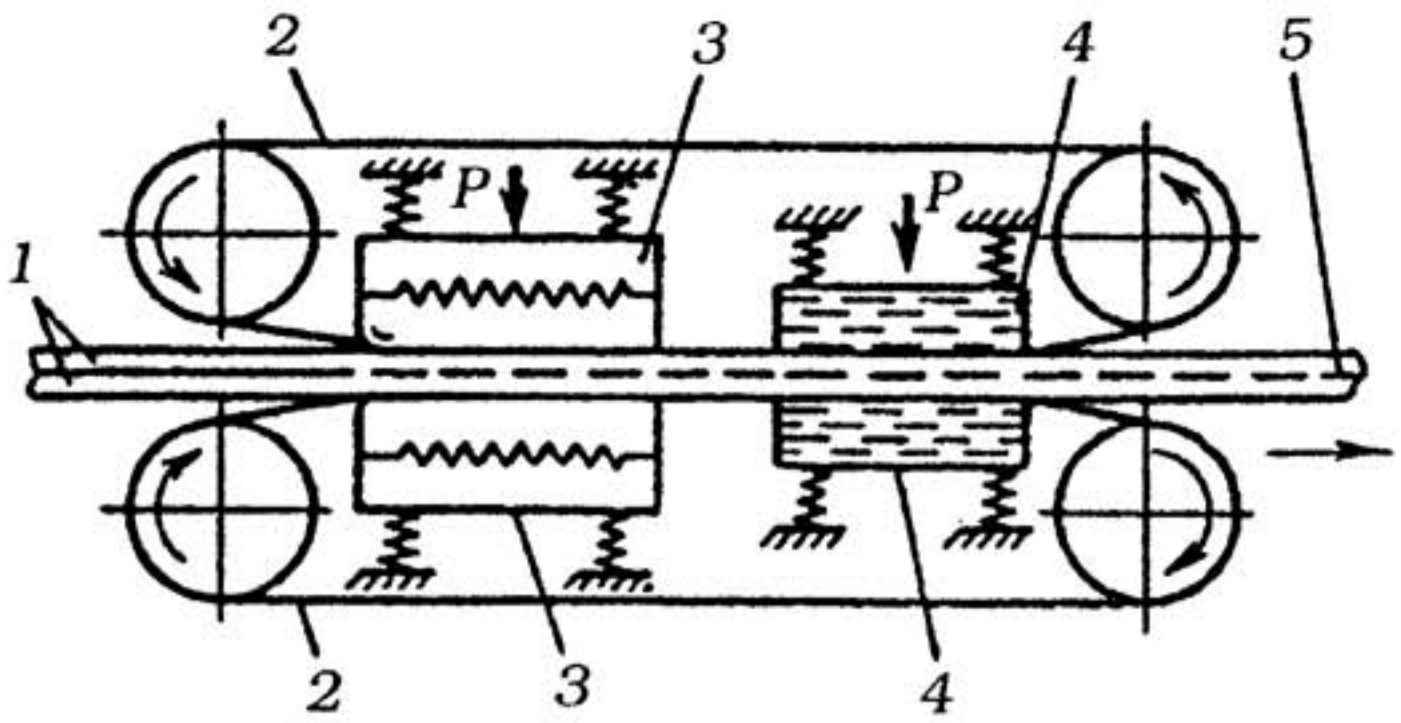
Схема ленточной двусторонней контактно-тепловой сварки: 1 — свариваемый материал; 2 — стальная лента; 3 — нагревательные губки; 4 — охлаждающие губки; 5 — сварной шов
